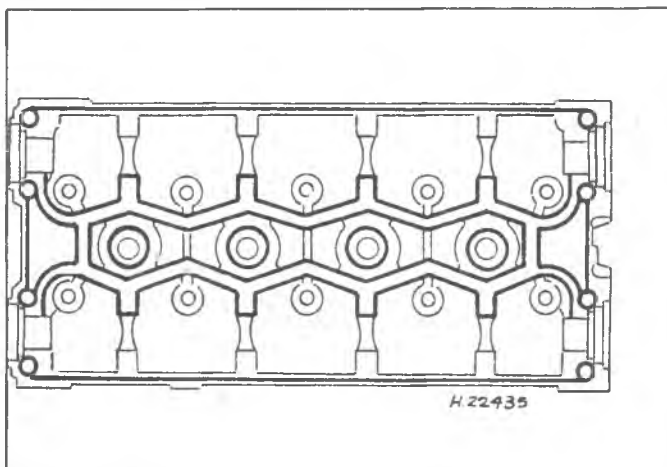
Нанесите валик герметика на выделенную зону стыковочной поверхности корпуса подшипников
